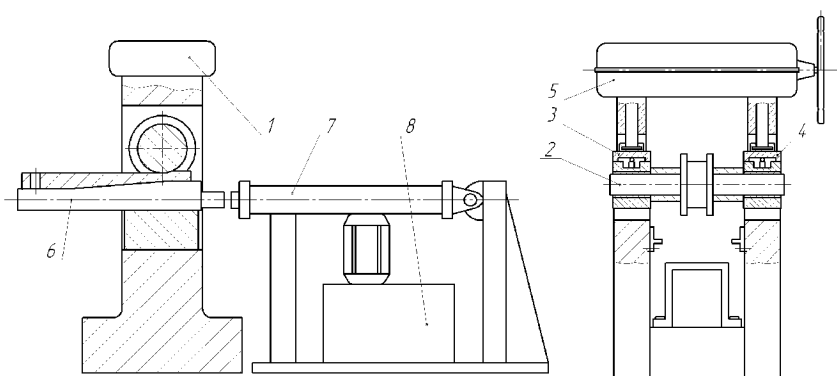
Схема экспериментальной установки для моделирования процесса прокатки заготовок направляющих опор
